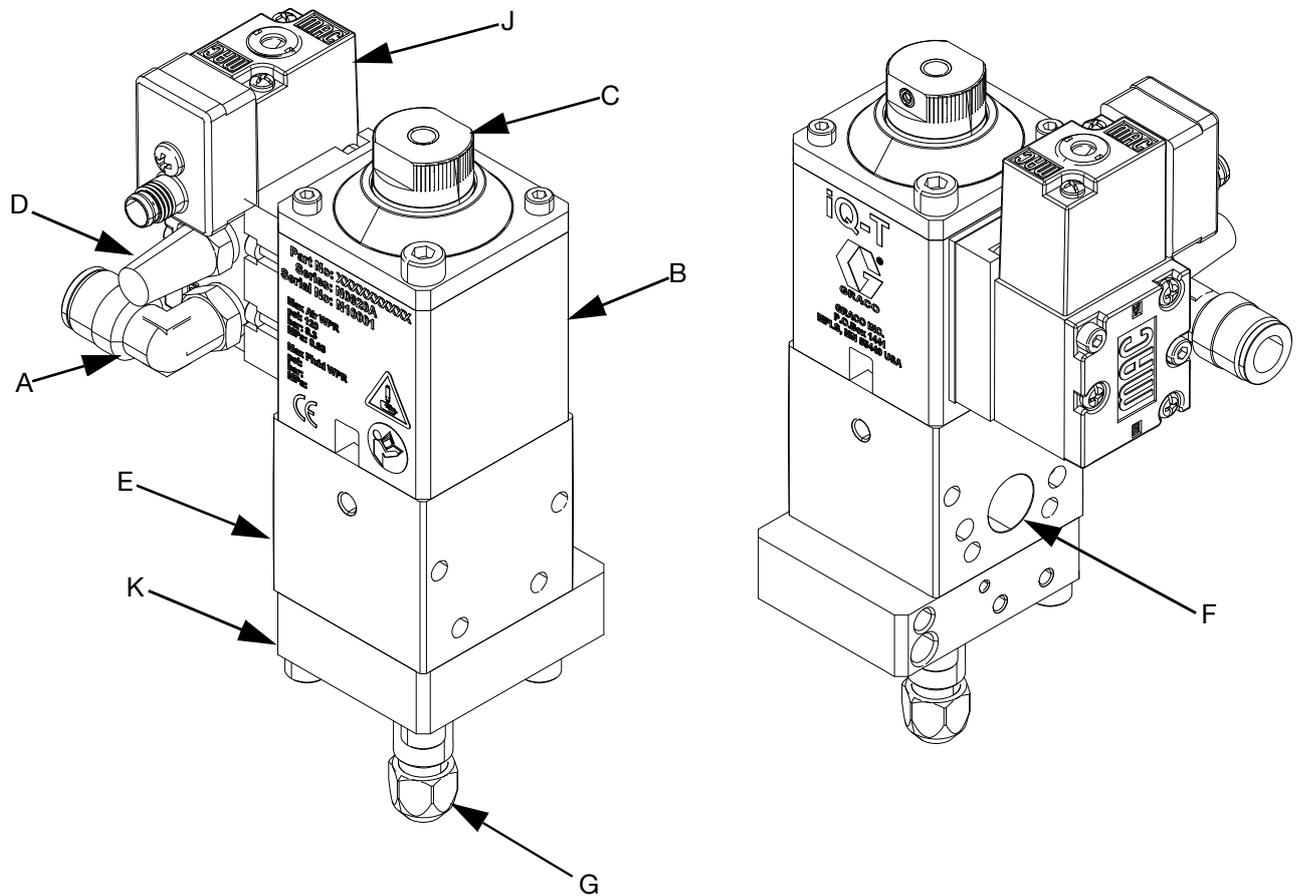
Válvula dispensadora de junta de boquilla VGMFT000BA de PGM
